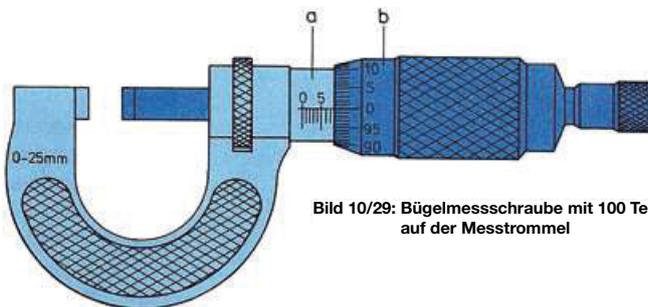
/29: Bügelmessschraube mit 100 Teilstrichen auf der Messtrommel
